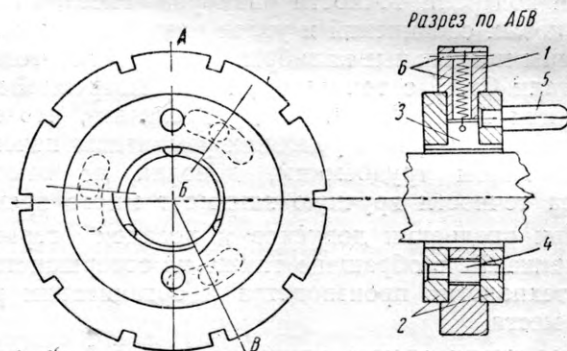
Делительная головка приспособления для фрезерования канавок на колонках:
